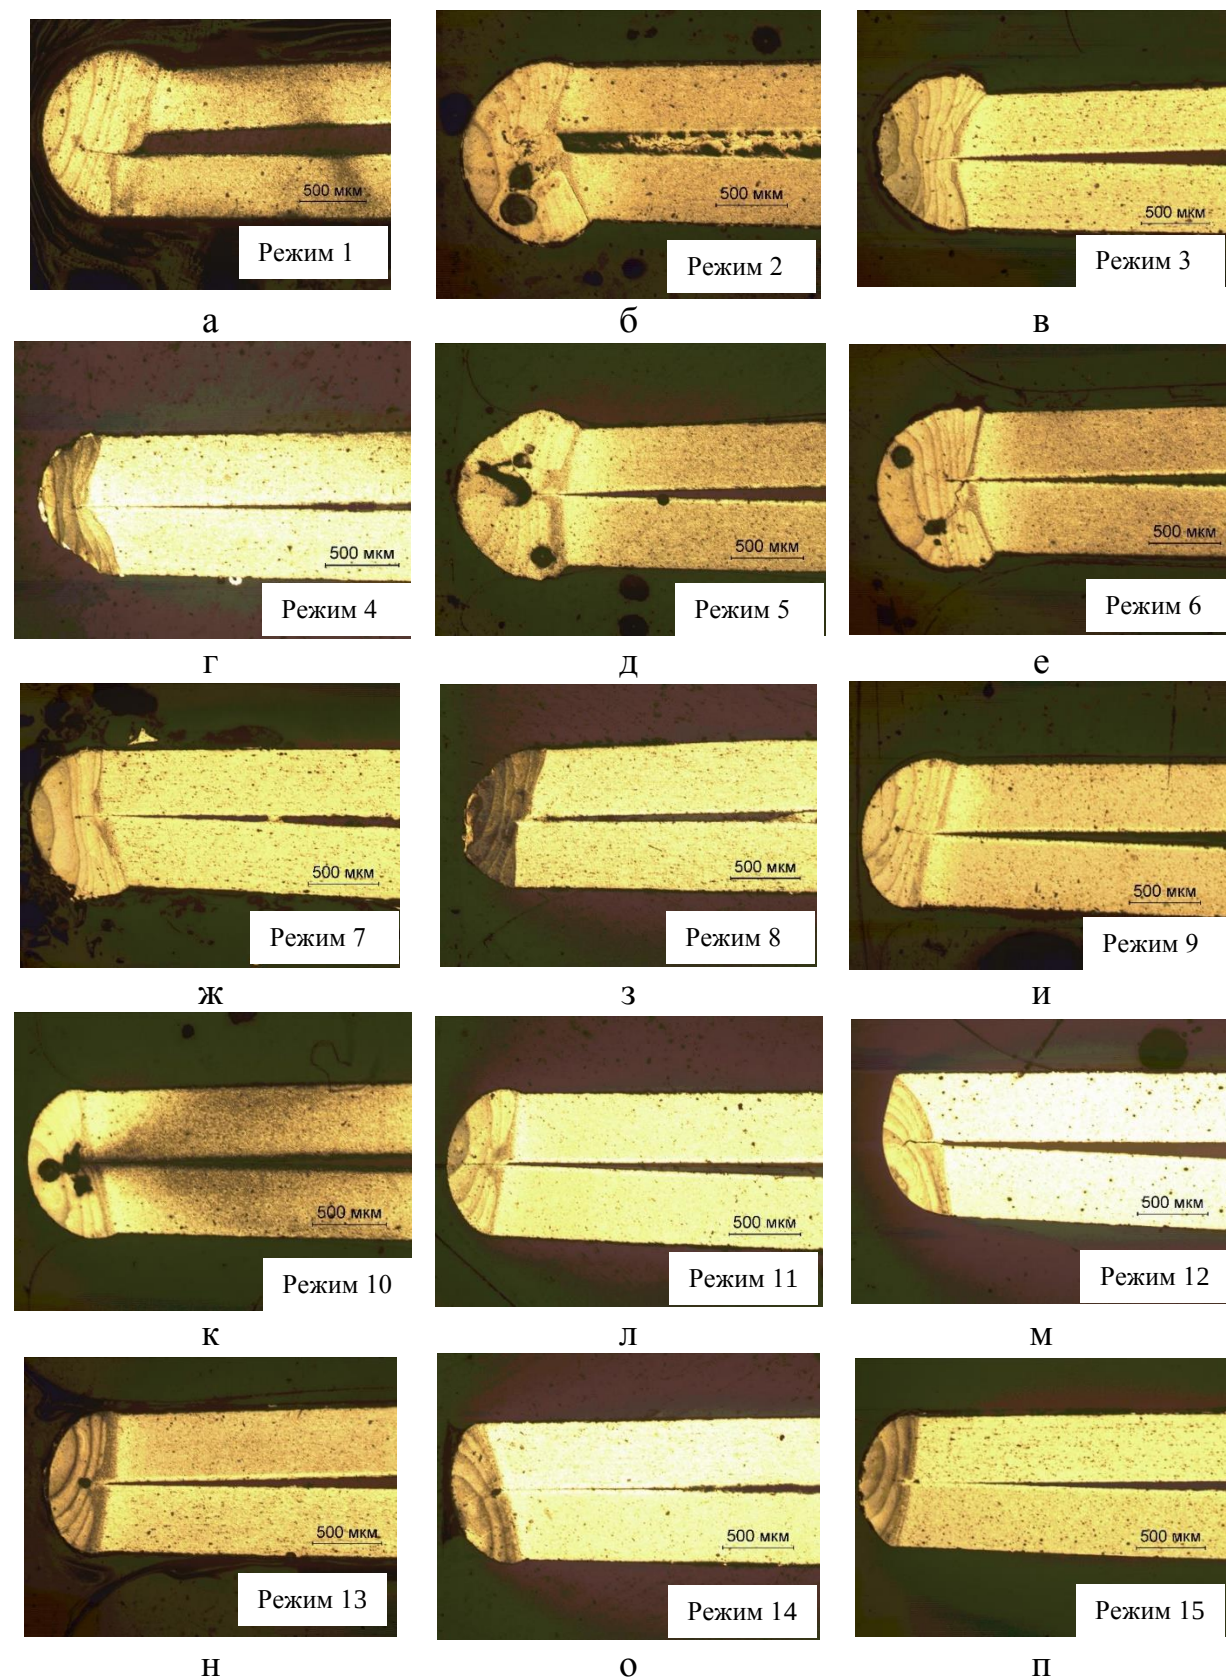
Макроструктура сварных соединений
